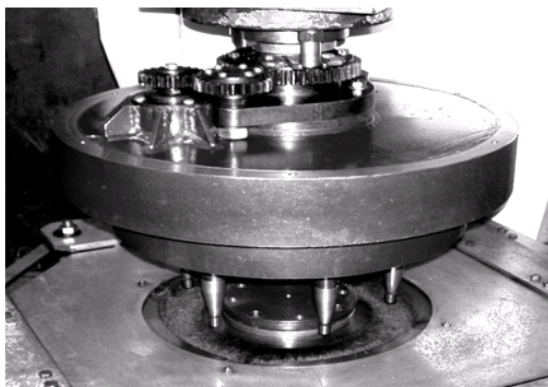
Внешний вид головки для обработки непереключаемых сменных твердосплавных пластин
